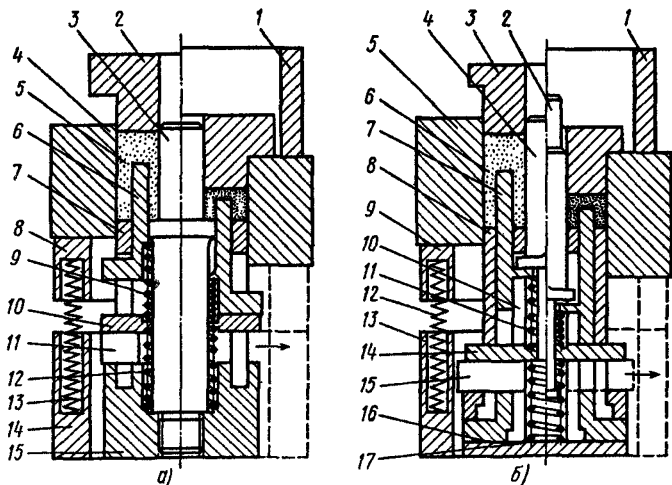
Схемы пресс-форм для прессования изделий с кольцевым пазом:
